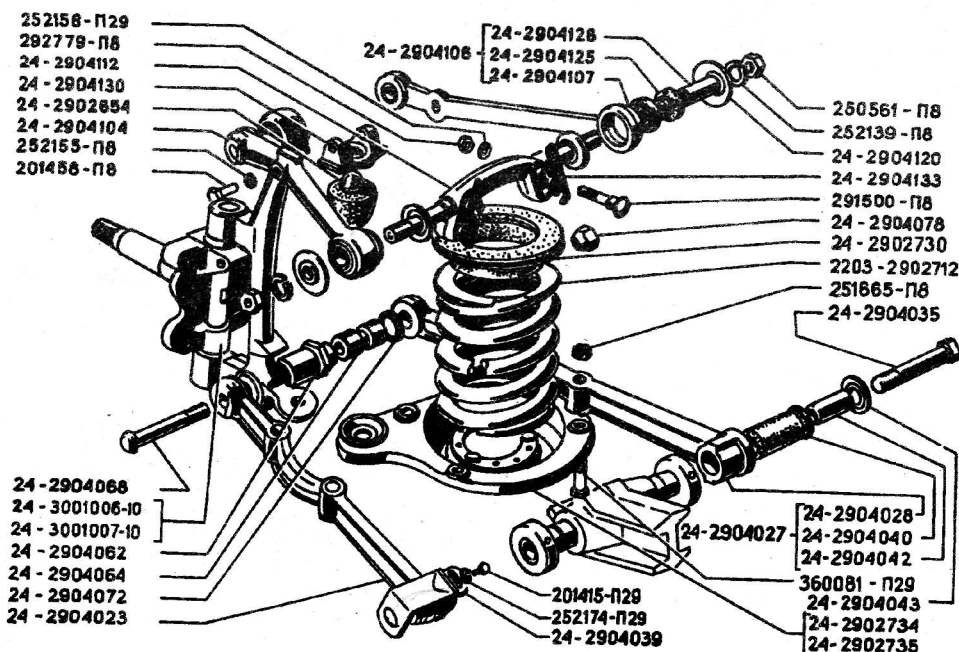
Подвеска передняя в сборе; рессоры передние; стойки и рычаги
